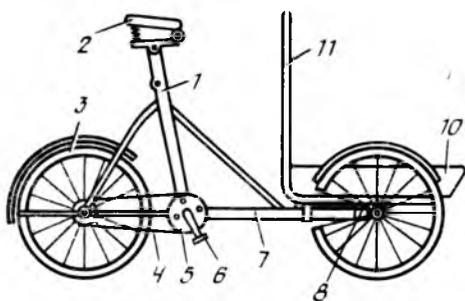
1 — каркас; 2 — седло; 3 — задние колеса; 4 — цепь; 5 — звездочка; 6 — педали; 7 — поворотный кронштейн; 8 — ведущий шарнир; 9 — рама тележки; 10 — кузов; 11 — руль; 12 — ограничитель поворота; 13 — ось колес
